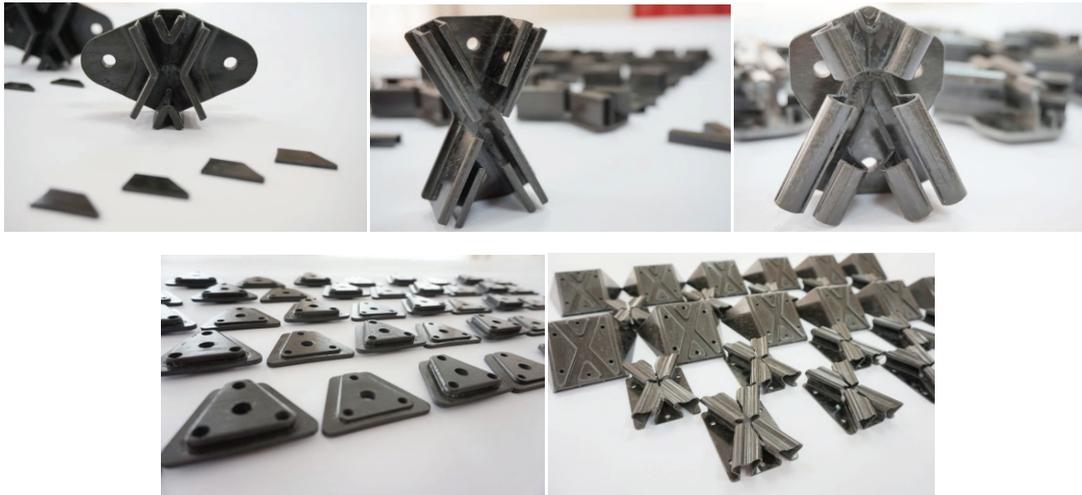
Виды элементов крепления для установки оборудования КА на силовую конструкцию корпуса
